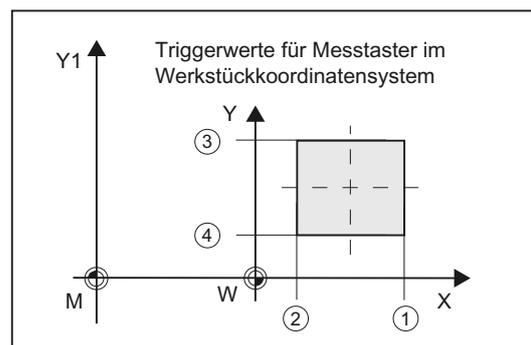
Werkzeugmesstaster, werkstückbezogen (G17)
